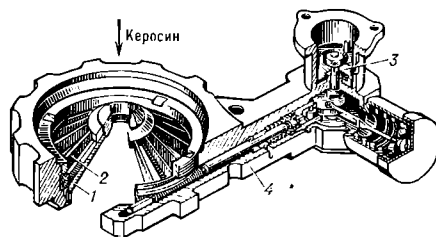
Дроссель системы опорожнения топливных баков (ЖРД РД-111): 1 — неподвижная решётка; 2 — подвижная решётка; 3 — полумуфта для присоединения электропривода; 4 — шток для поворота решётки
